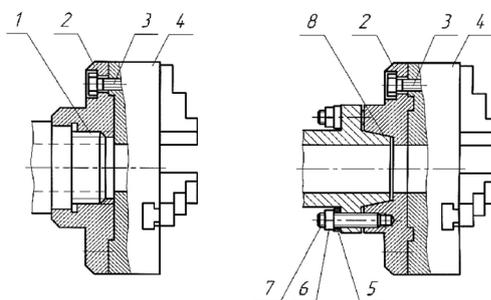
Закрепление токарного патрона на шпинделе станка:
